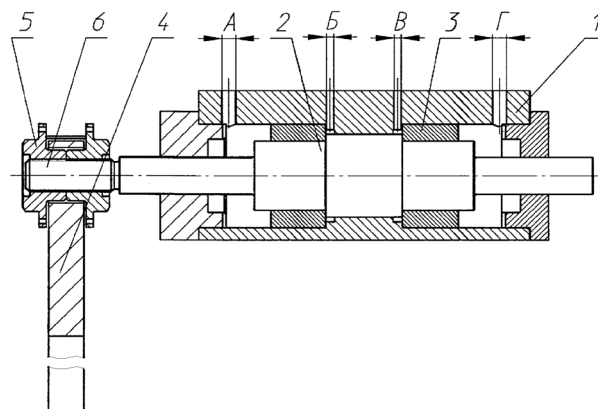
Гидравлический цилиндр перемещения вилки переключения передач: 1 — корпус; 2 — ступенчатый поршень; 3 — дополнительный поршень; 4 — вилка; 5 — гайка; 6 — резьбовой конец штока ступенчатого поршня
